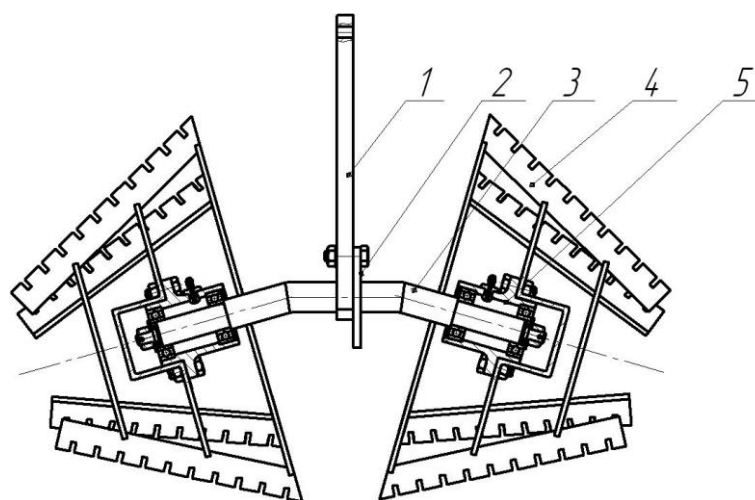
Сборочный чертеж ротационного рыхлителя
